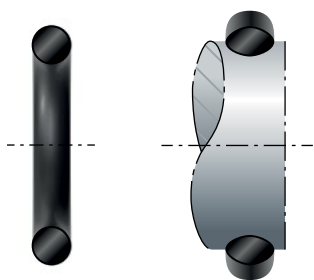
links: ungedehnter O-Ring, rechts: gedehnter O-Ring
